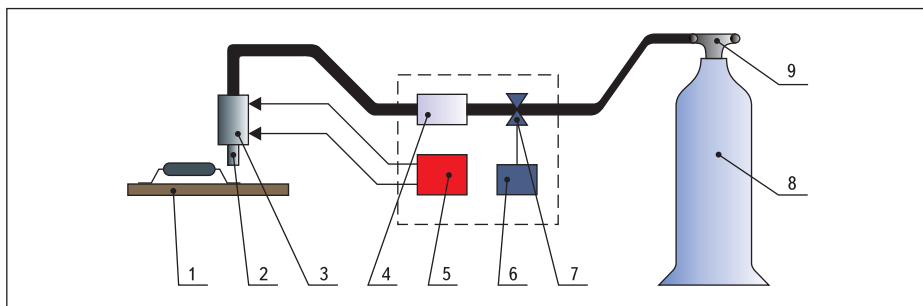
Установка для монтажа и демонтажа газовым нагревателем: 1 — печатная плата с компонентами; 2 — насадка; 3 — нагреватель; 4 — датчик контроля потока газа; 5 — источник питания нагревательного элемента; 6 — система управления клапаном; 7 — клапан регулировки потока газа; 8 — баллон с газом; 9 — редуктор
